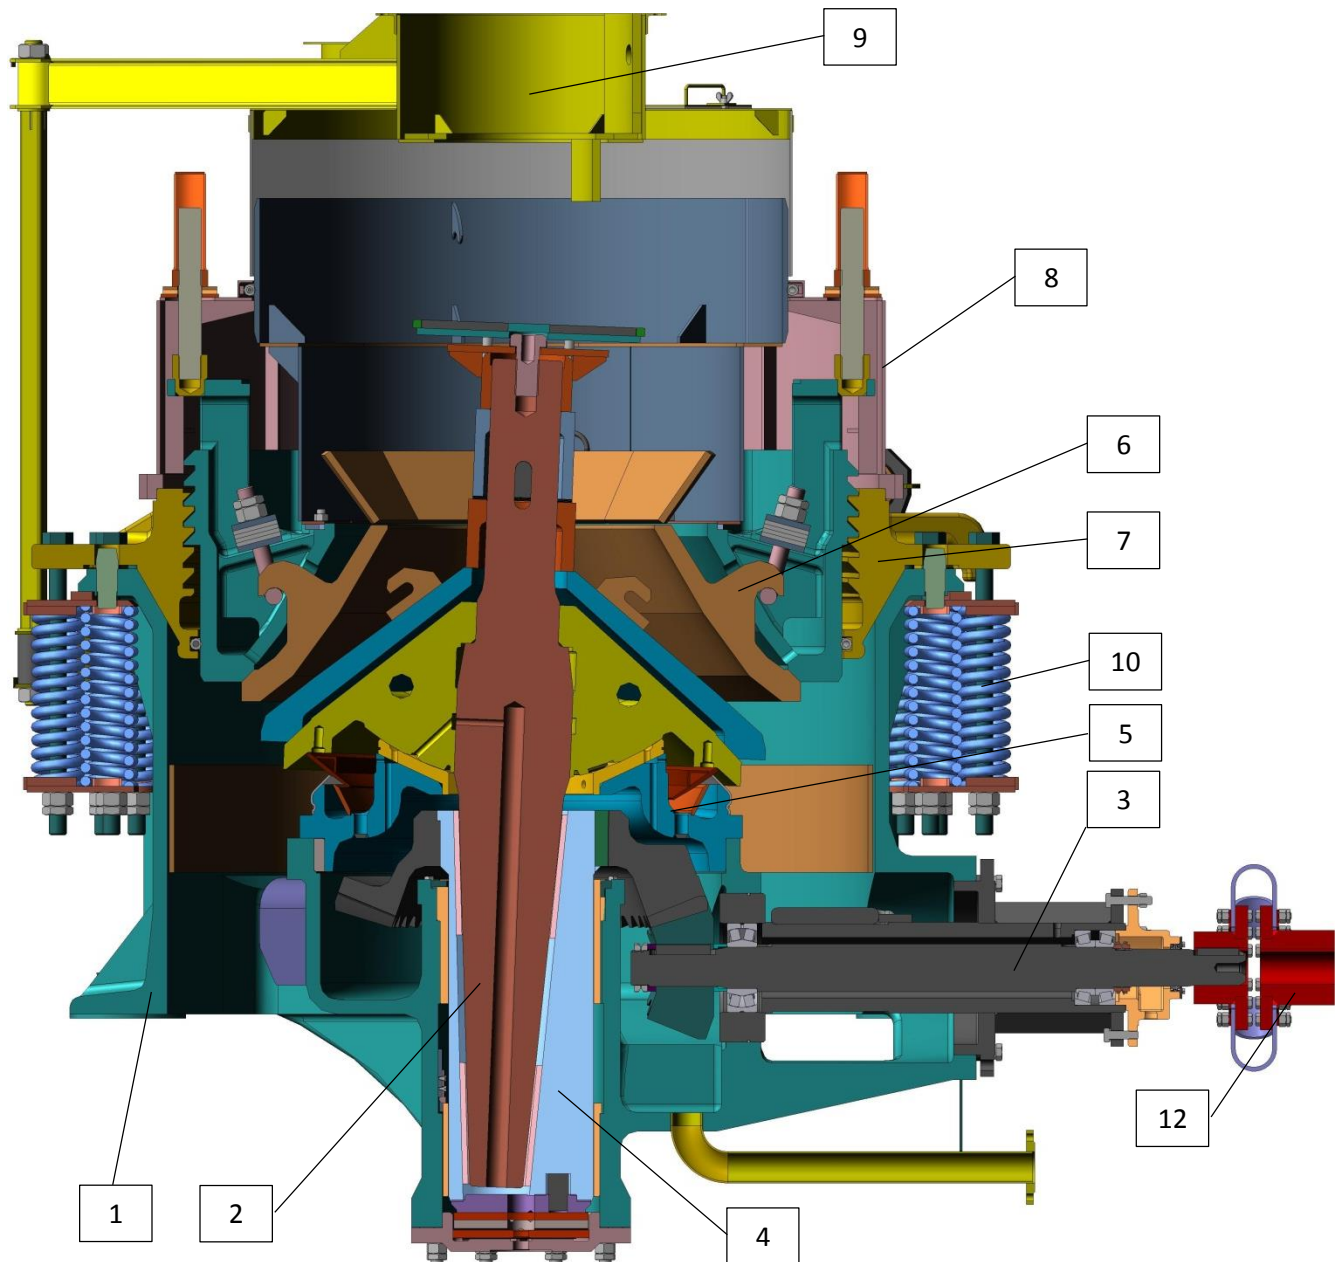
Механизм дробилки 1200. Общий вид в разрезе.
